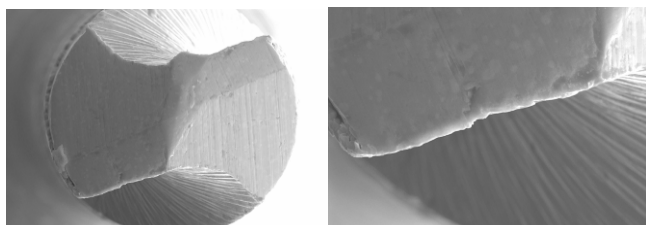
REM-Aufnahmen des Bohrers $d = 0,25$ mm
